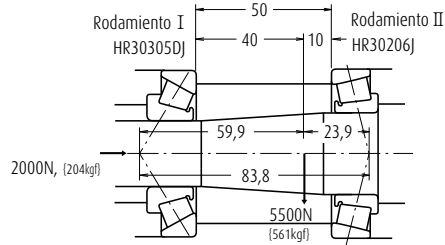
Cargas sobre rodamientos de rodillos cónicos
